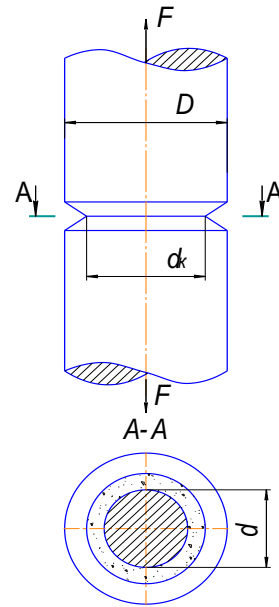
Осьовий розтяг циліндричного зразка з кільцевою тріщиною.
